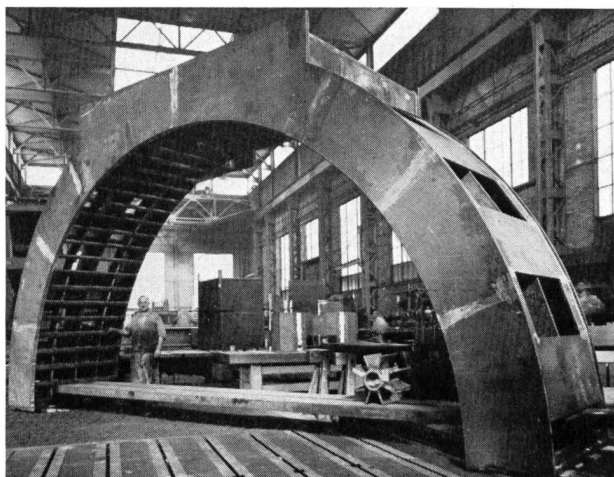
Demi-stator d'alternateur à axe vertical, de construction soudée, avant son usinage (Photo Sécheron)
